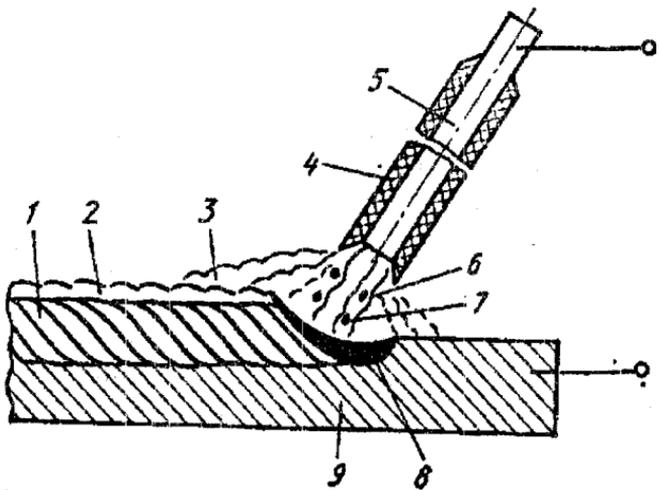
Схема ручного дугового зварювання металевим покритим електродом: 1 – зварний шов; 2 – шлакова кірочка; 3 – захисна газова атмосфера; 4 – електродне покриття; 5 – електродний стрижень; 6 – електрична дуга; 7 – краплі електродного металу; 8 – зварна ванна; 9 – заготовка
